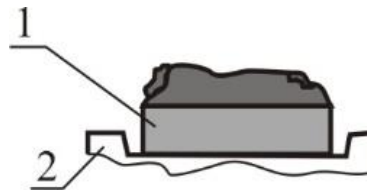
Схема реконструювання твердосплавної напайки циліндричним інструментом
